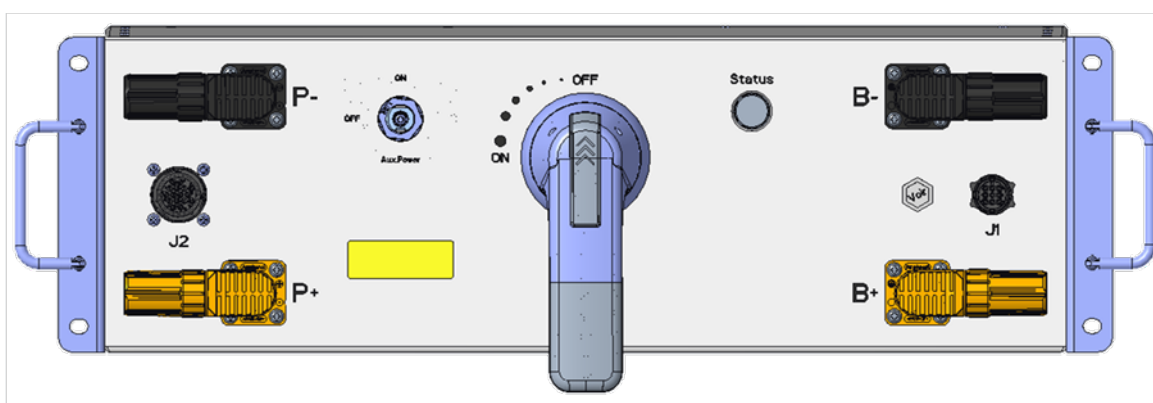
Caja de aislamiento de la batería de alta tensión (QB desconectado)
